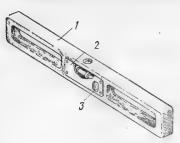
1 — корпус; 2 — ампула, 3 — винт; 4 — крышка
